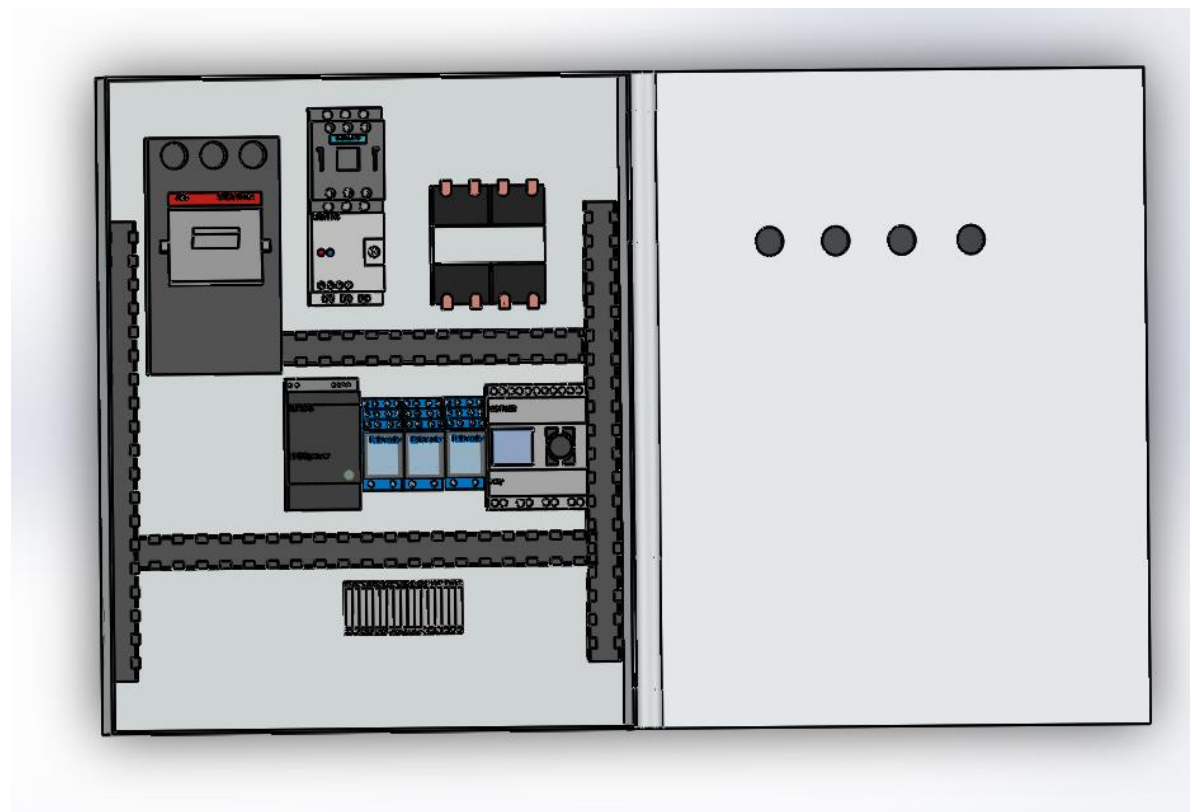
actual tablero de control de maquina compactadora realizado en Solidworks con medidas reales de sus diferentes componentes.
